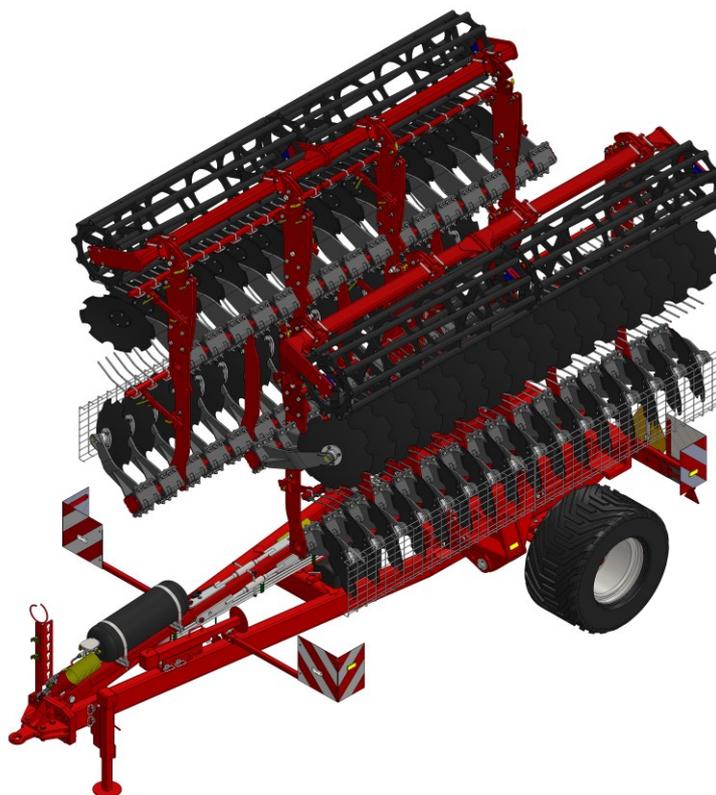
Posición de transporte con dispositivos de protección para los elementos de trabajo (secciones laterales plegadas)
